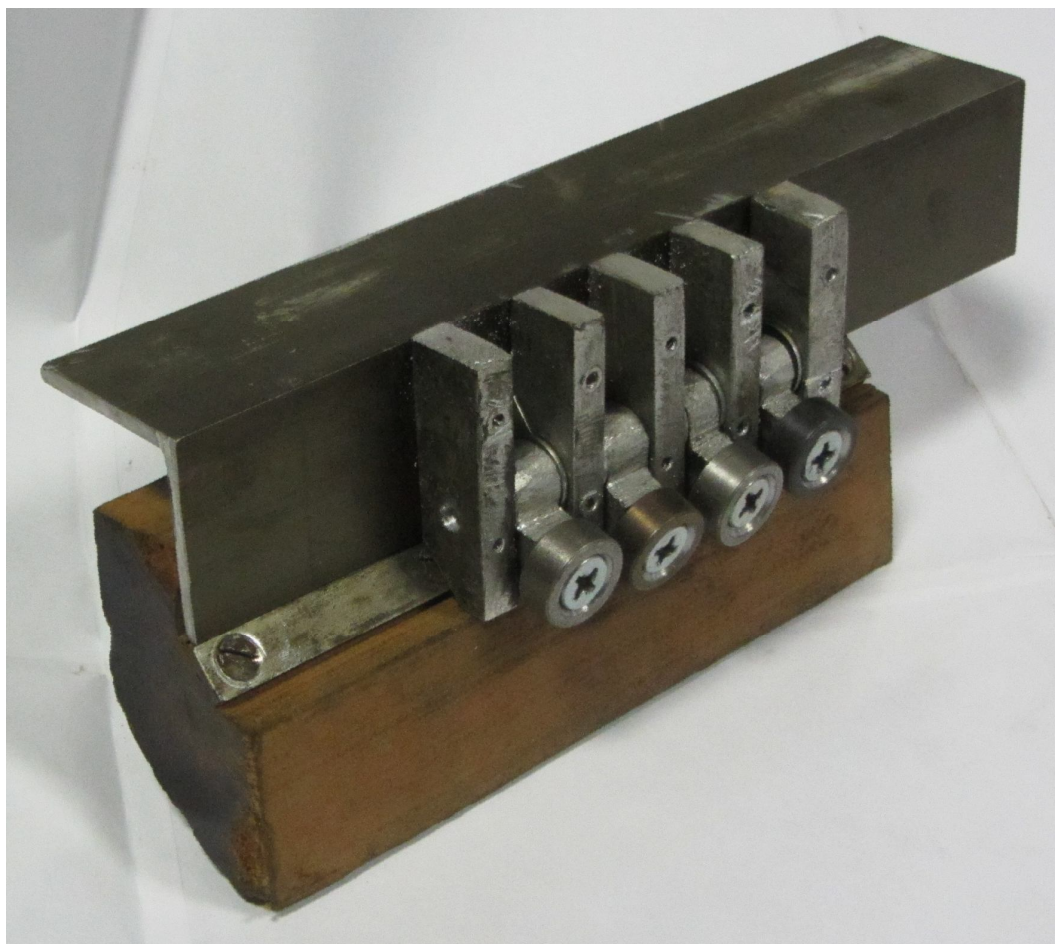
Секция корпуса разливочного устройства с установленными в ней поворотными прижимными элементами, снабженными роликами
